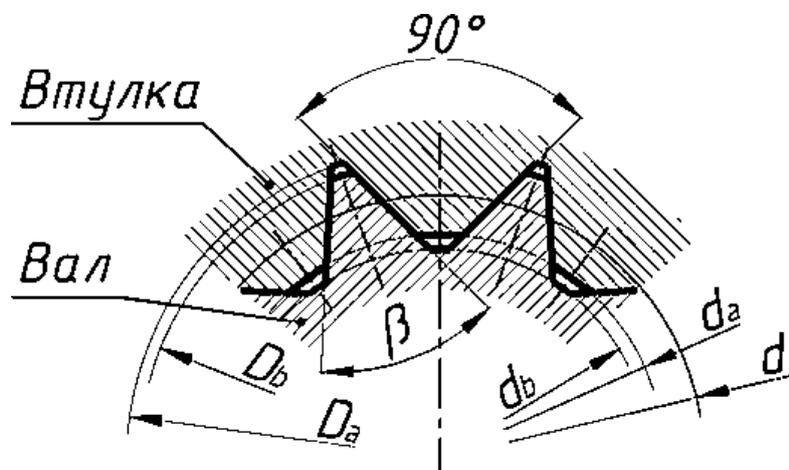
Образец изображения шлицевого соединения с треугольным профилем.
